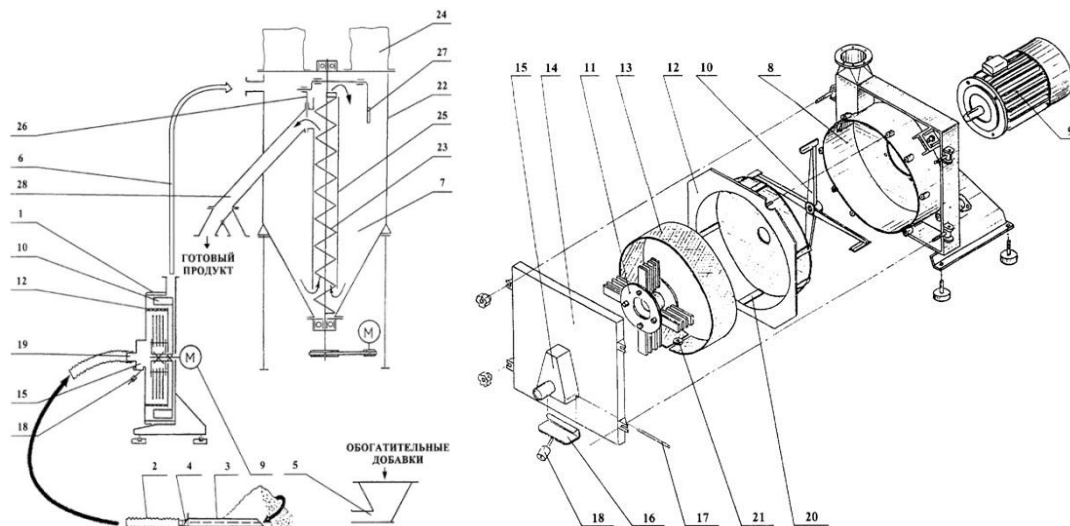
Малогабаритный комбикормовый агрегат: 1 – дробилка; 2 – гибкий рукав; 3 – насадка; 4 – заслонка; 5 – питатель; 6 – пневмопровод; 7 – смеситель-накопитель; 8 – корпус; 9 – электродвигатель; 10 – вентилятор; 11 – молотковый ротор; 12 – каркас; 13 – решето; 14 – крышка; 15 – камера; 16 – заслонка; 17 – ось; 18 – подвижный груз; 19 – патрубок; 20 – стойки; 21 – фиксатор; 22 – корпус; 23 – шнек; 24 – фильтра; 25 – кожух; 26 – задвижка; 27 – рукоятка; 28 – патрубок
